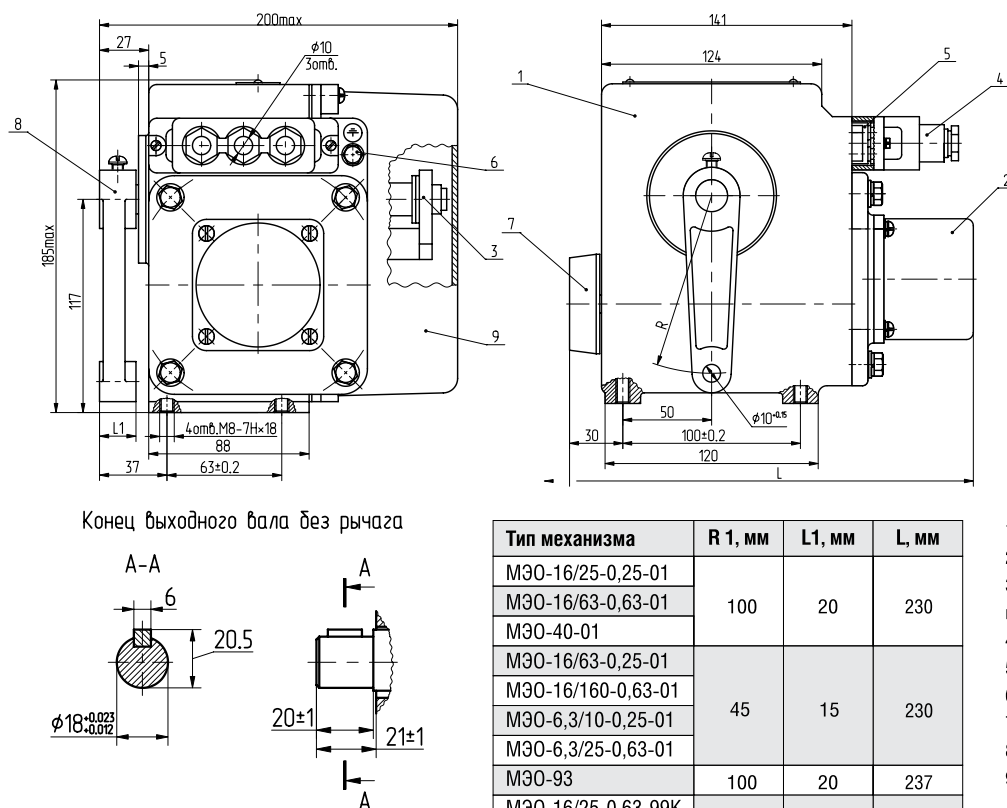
Габаритные и присоединительные размеры М30-6,3
